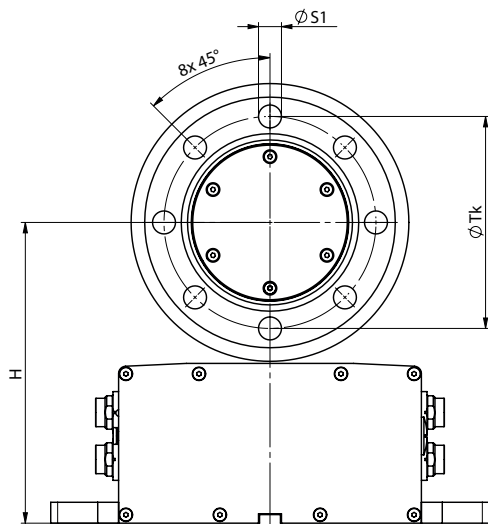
Maßzeichnung Ansicht A, KiTorq System
